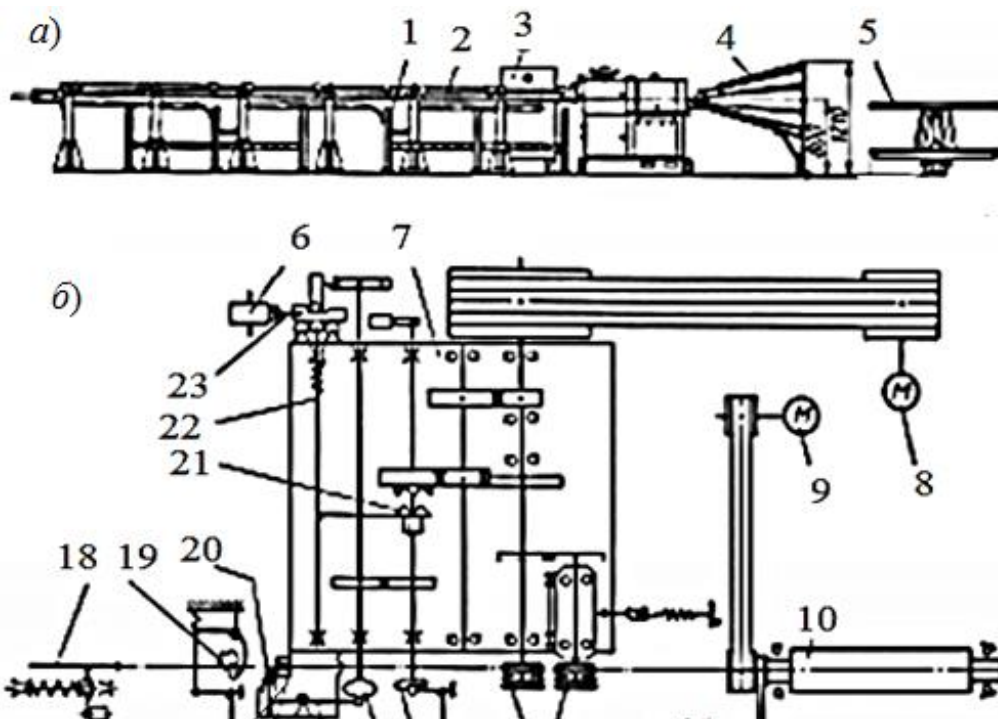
Станок для одновременной правки и резки арматурной стали с непрерывной подачей: *а* – общий вид: *б* – кинематическая схема.
